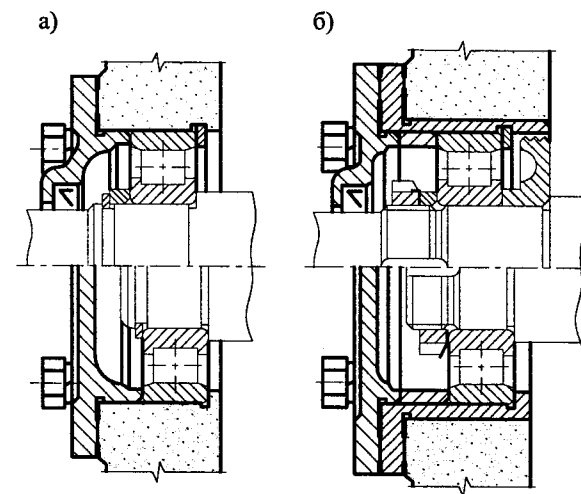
Установка наружного кольца разъемного подшипника в корпусе плавающей (самоустанавливающейся) опоры
